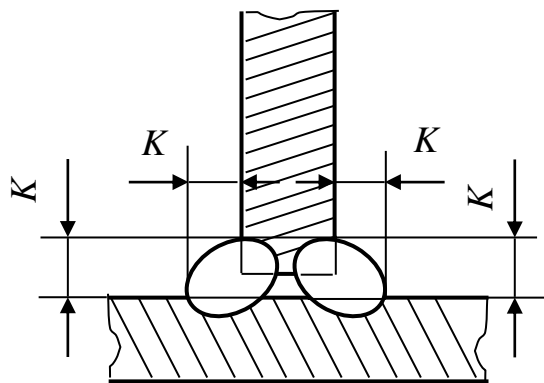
Зварний шов № 2, з'єднання Т3
